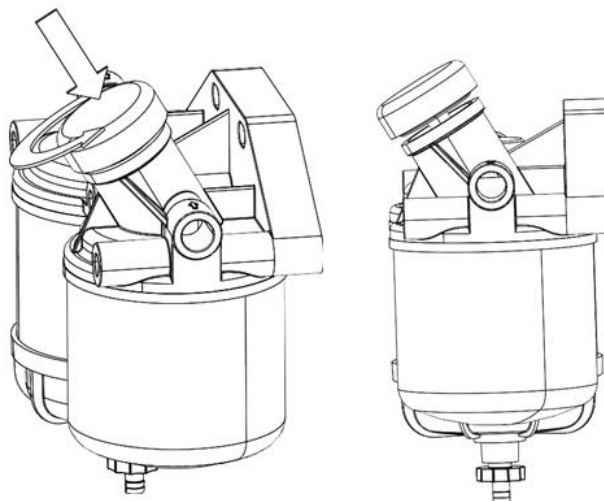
Топливный фильтр с самоблокирующейся конструкцией плунжера ручного насоса.
